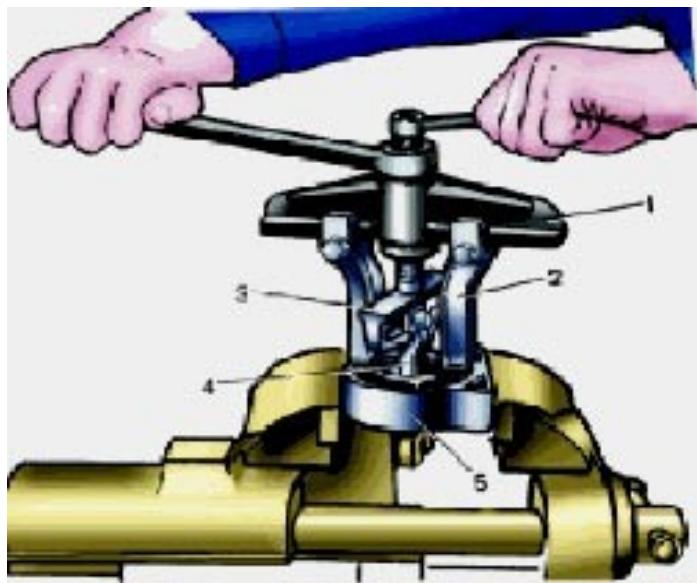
Випресування підшипника з проміжної опори:
